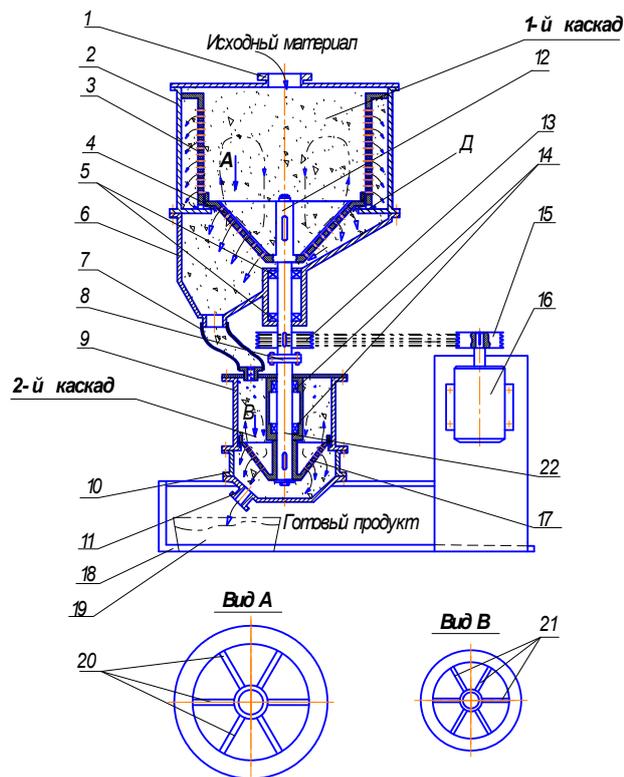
Двухкаскадная мельница динамического самоизмельчения: 1 – загрузочный патрубкок; 2 – верхний корпус; 3 – внутренняя перегородка; 4 – чаша верхнего ротора; 5 – верхний подшипниковый узел; 6 – сборная камера; 7 – гибкий соединительный канал; 8 – полумуфта; 9 – нижний корпус; 10 – нижняя сборная камера; 11 – выгрузной патрубкок; 12 – верхний вал; 13 – ведомый шкив; 14 – нижний подшипниковый узел; 15 – клиновой ремень; 16 – ведущий шкив; 17 – электродвигатель; 18 – чаша нижнего ротора; 19 – рама; 20 – сборная емкость; 21 – ребро верхней чаши ротора; 22 – ребро нижней чаши ротора
